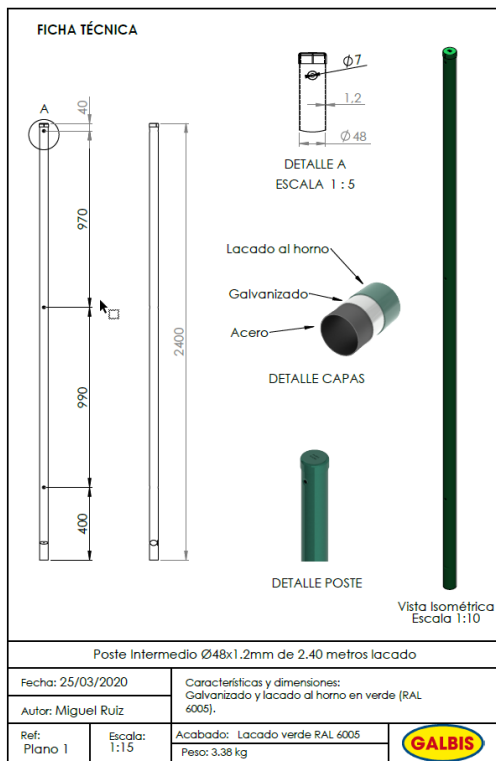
Vedação Postes Metálicos e Rede Metálica Elástica
